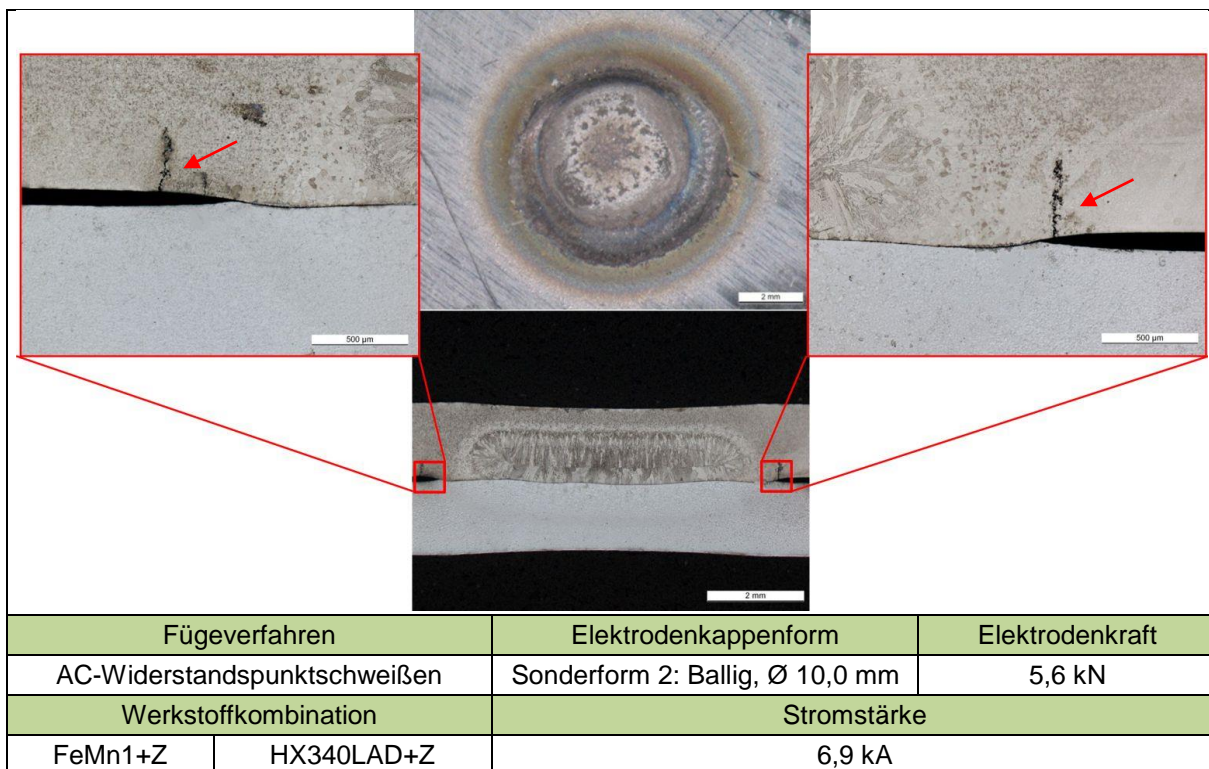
FeMn1+Z/HX340LAD+Z: Makroaufnahmen und Querschliffe, geschweißt mit Elektrodenkappe Sonderform 2 (ballig, Ø 10,0 mm) und Elektrodenkraft 5,6 kN
